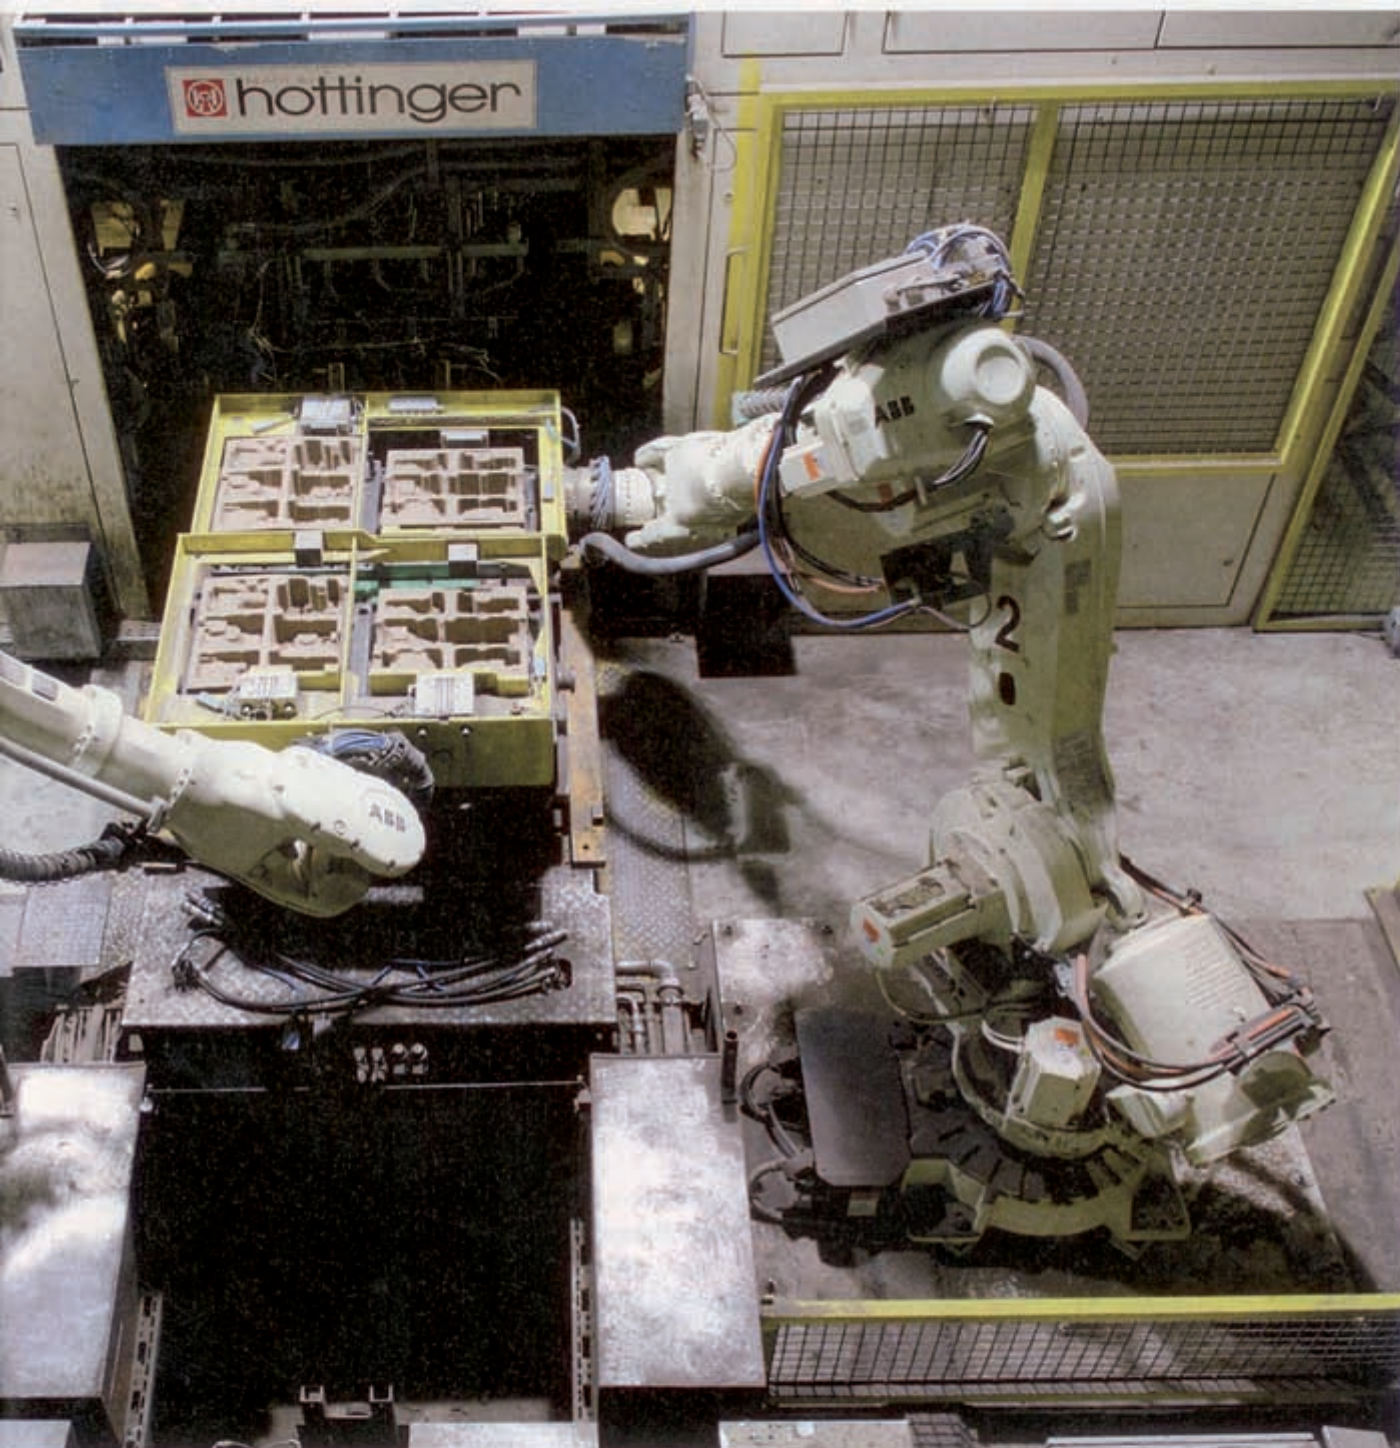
(oben): Zwei Roboter entnehmen gleichzeitig vier Kurbelraum- bzw. Seitenkerne aus dem Werkzeug.
